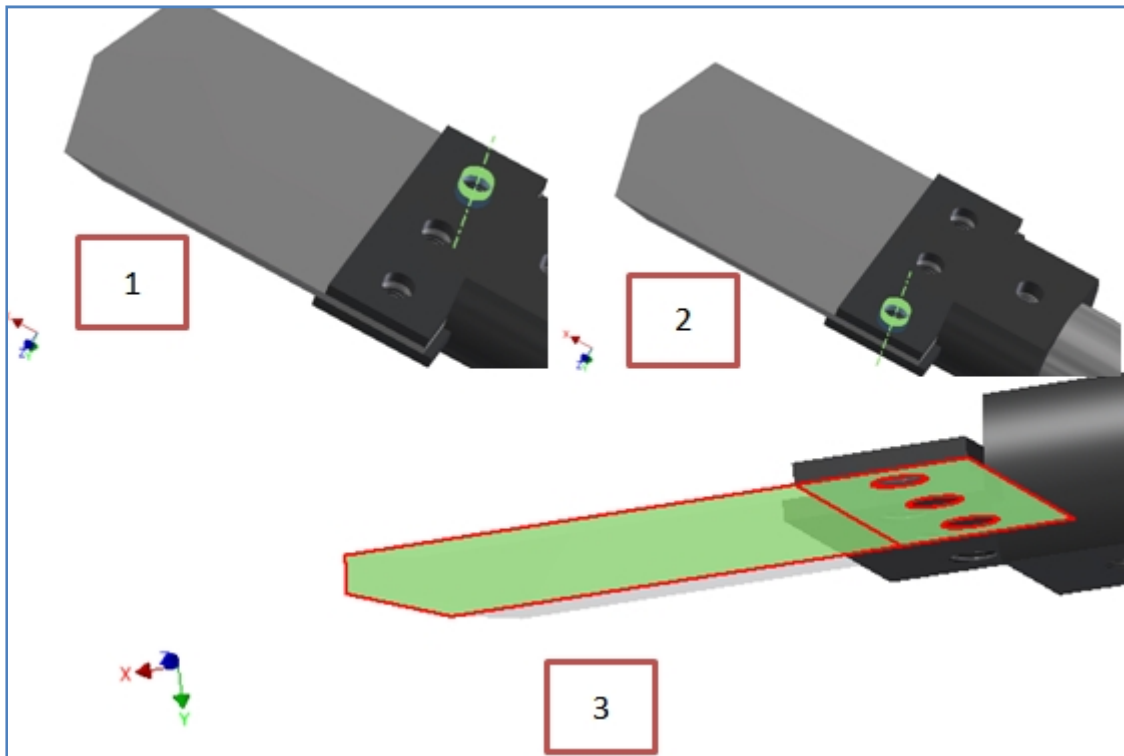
Selección de caras para el procedimiento de ensamblaje de la cuchilla sobre el conjunto previamente ensamblado.
